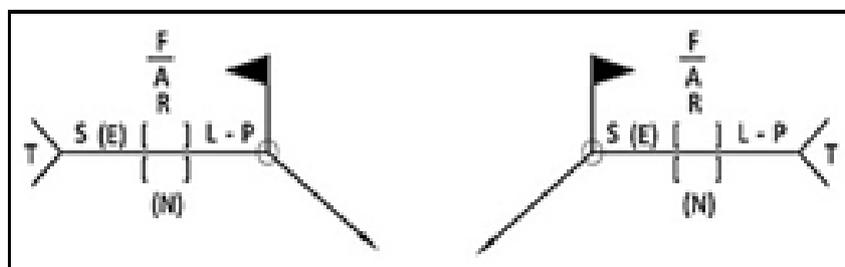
Esquema de la información que puede contener el símbolo de una soldadura.
